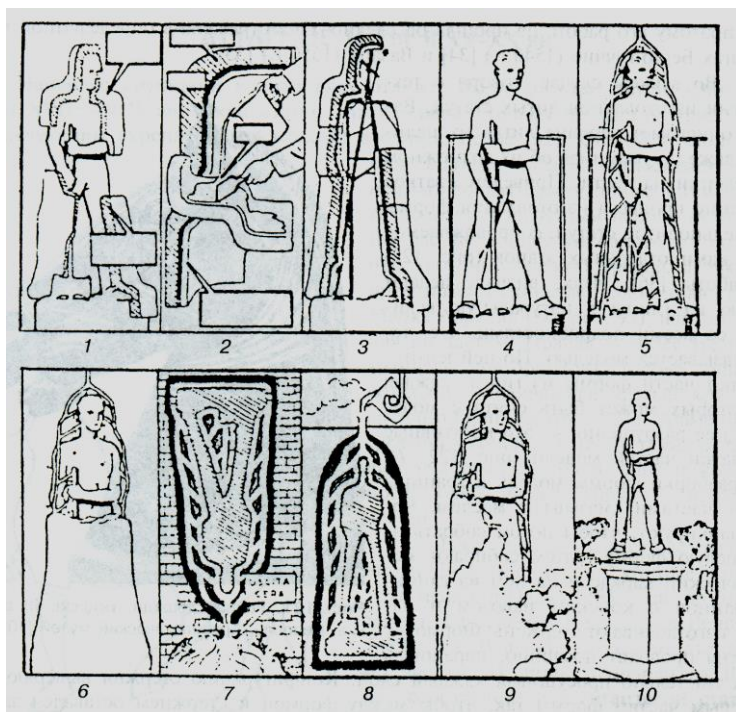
Этапы изготовления цельнолитых статуй по Вазари
